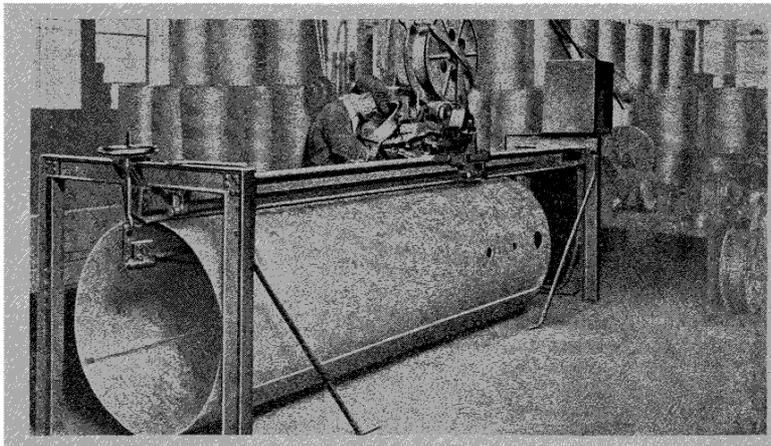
Machine automatique pour la soudure longitudinale des réservoirs de stock d'essence de 2.500 litres.
